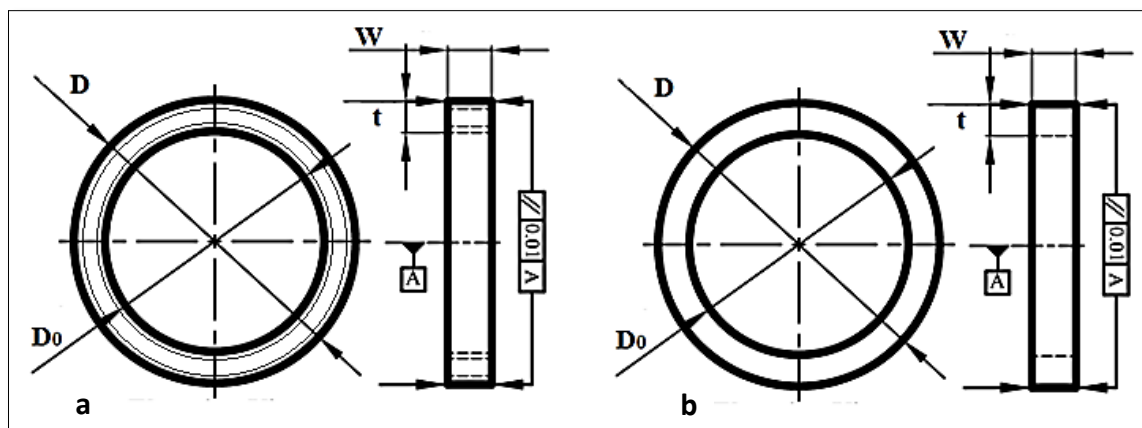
Géométrie des éprouvettes sous forme d'anneaux.
